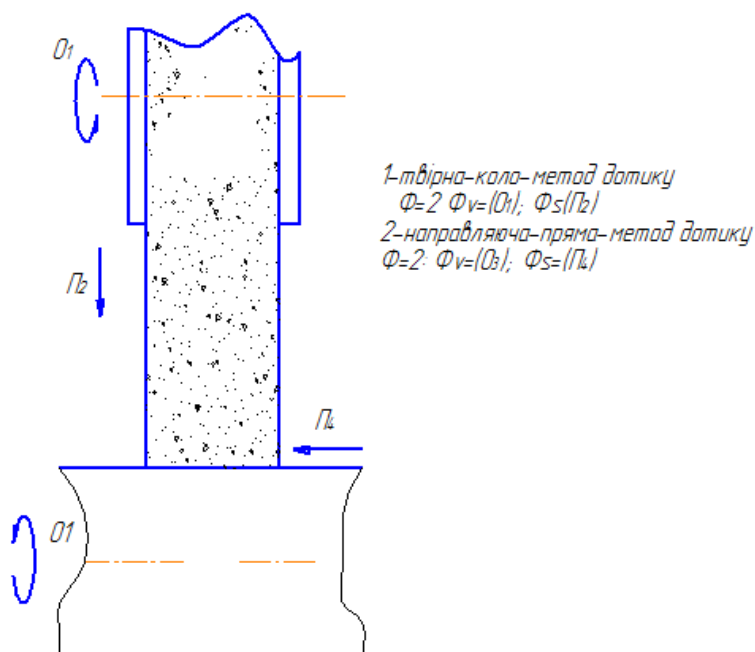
Комплекс формоутворюючих рухів при обертovому русі заготовки та інструменту (операція шліфування)
